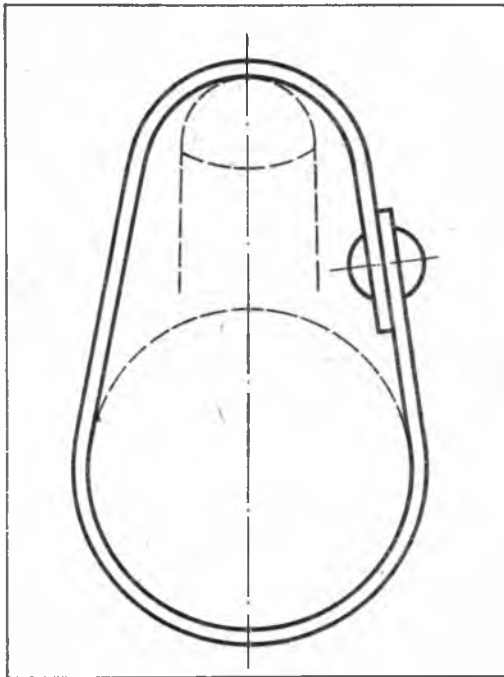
Кольцо, надеваемое на рукоятку стояночного тормоза, и рычаг декомпрессора при пуске двигателя
